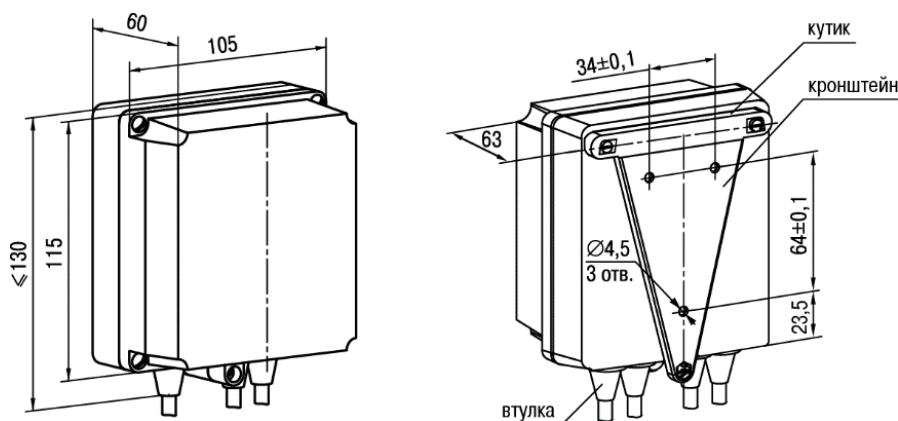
Габаритні та установчі розміри корпусу Н
